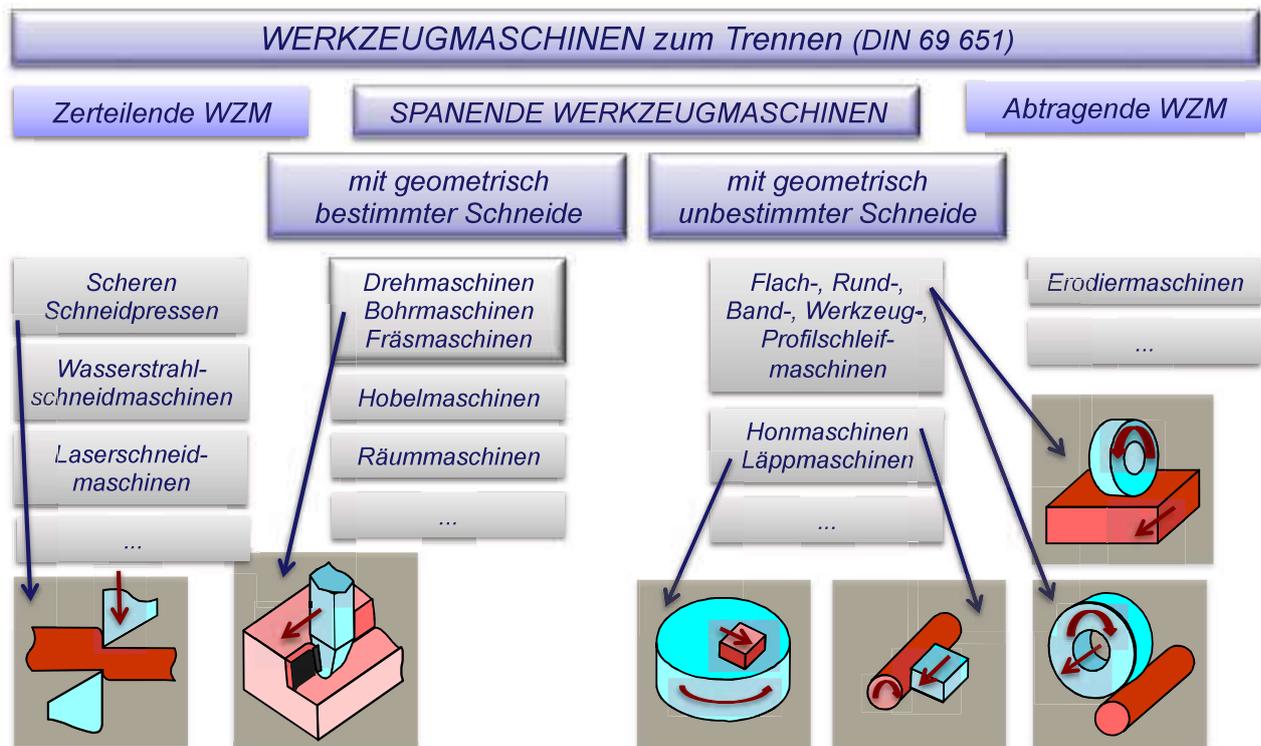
Einteilung der Werkzeugmaschinen zum Trennen (DIN 69 651)
